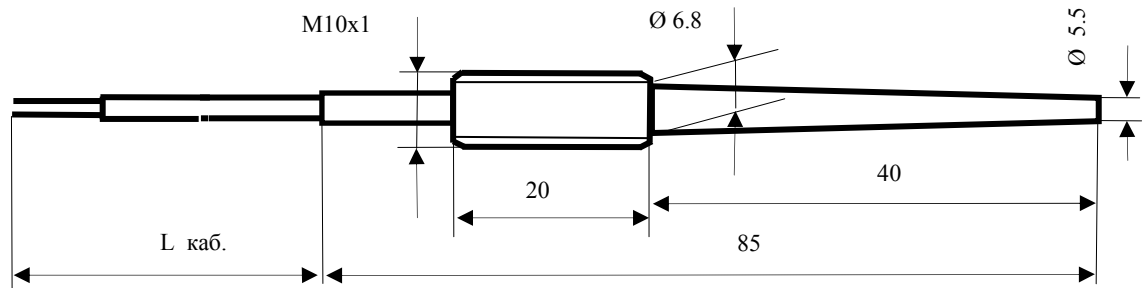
Габаритные и присоединительные размеры ТСП 002-04 модель 2
